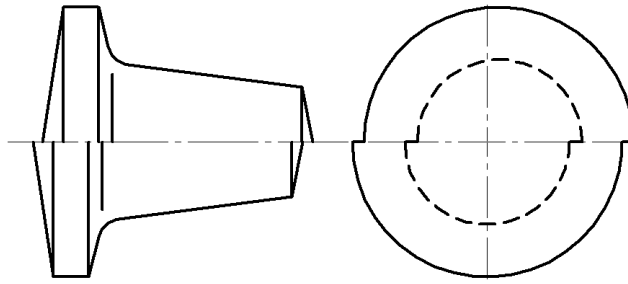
Поковка, яка одержана в штампах з роз'ємом в площині найбільшого перерізу заготовки
